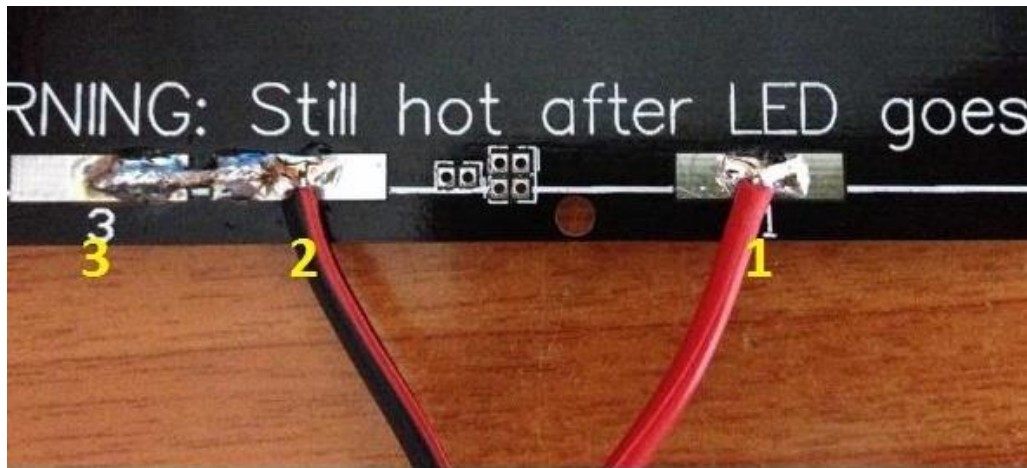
Conexión de la placa PCB. Montaje cama caliente, Zona Maker, Raul Desdeno
